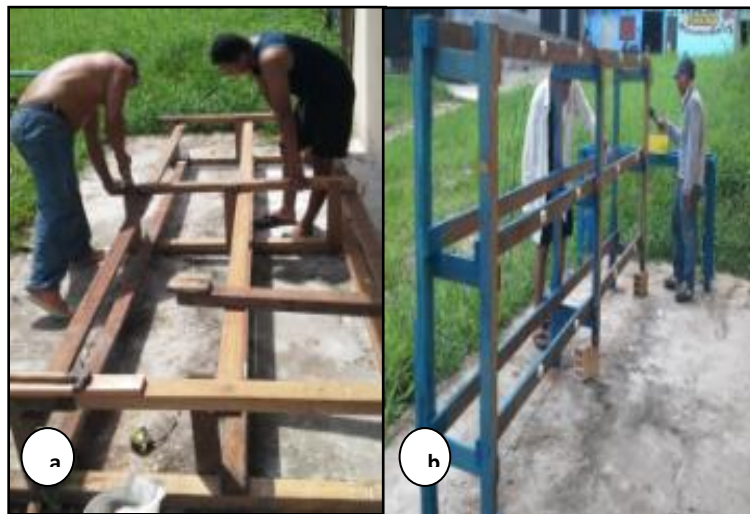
Construcción de estantes de madera - a. Armado, b. Pintado
